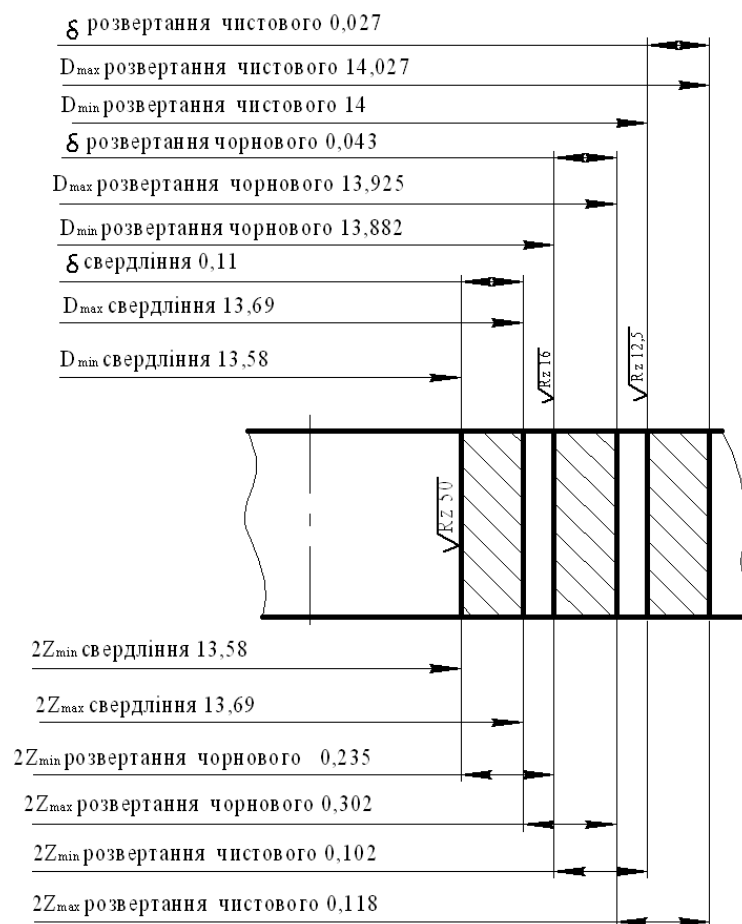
Схема розташування припусків та допусків при обробленні поверхні 14H8(^{+0,027})
